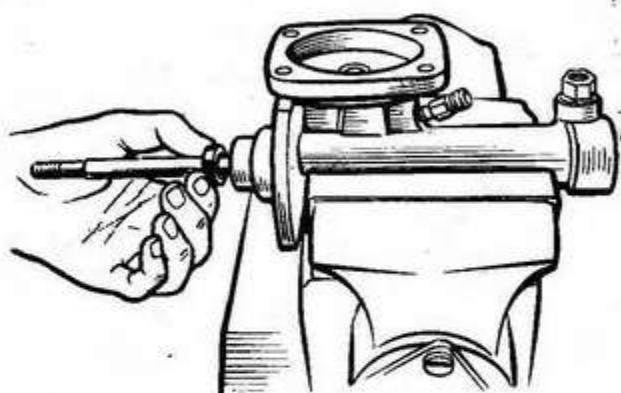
Установка вторичной манжеты в корпус уплотнителей
